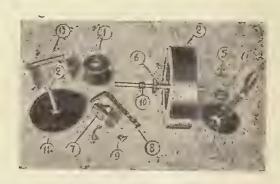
Детали установки т. Успенского: 1 барабан для записи; 2 — махоник; 3 и 4 — шестерии вубчатого механизма; 5-инит креплении большой шестерни; 6—червячнан шестерня центробежного регулятора; 7—центробежный регулятор; 8— стойка крепления центробежного регулятора; 9 — подпятник центробежного регулятора; 10 — резиновое кольцо фрикционного перебора механизма смещения рекордера; 11 н 12 фрикционный дяск в винт смещения рекордера; 13—кронштейн крепления винта смещении
